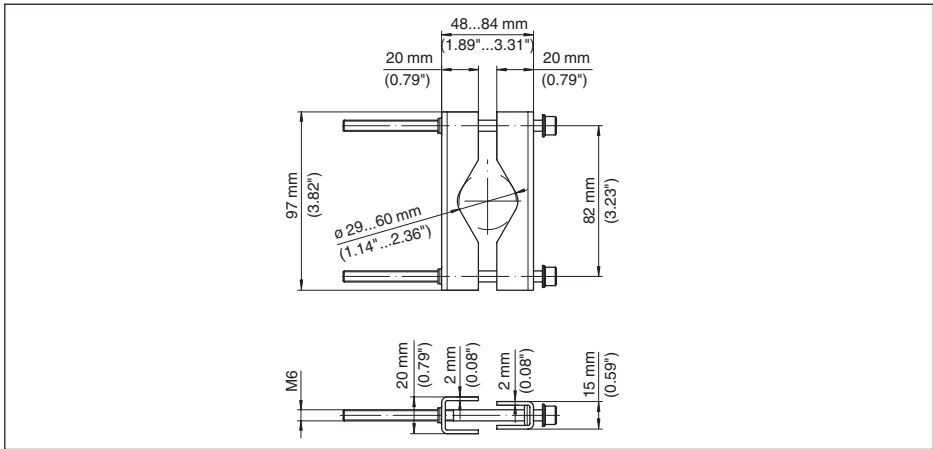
Suportes para montagem do VEGADIS 81 em tubo
